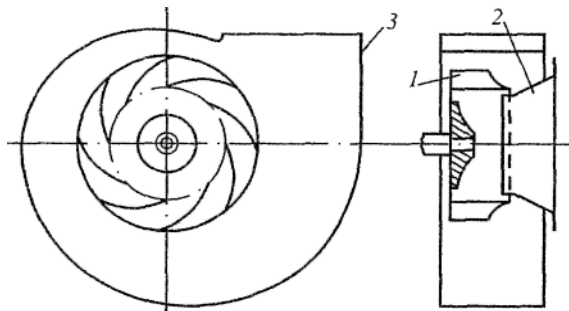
Аеродинамічна схема відцентрового вентилятора: 1 – робоче колесо; 2 – вхідний патрубок; 3 – спіральний корпус
